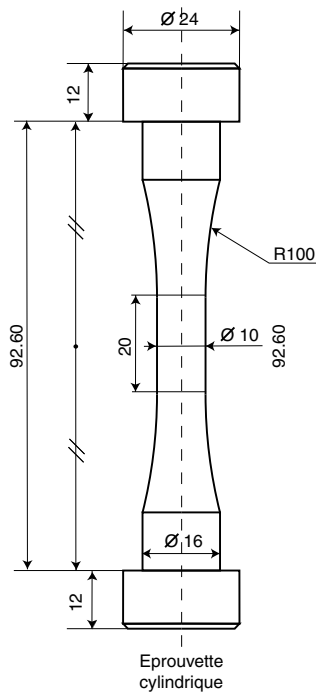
Géométrie des éprouvettes cylindriques.
